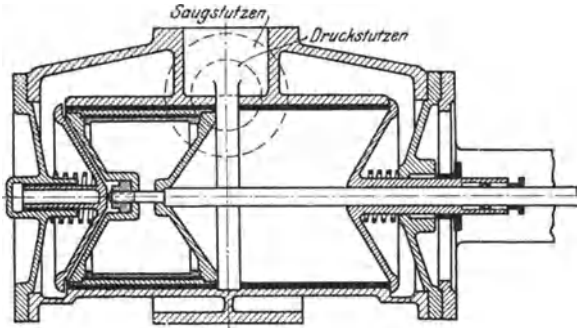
Christie-Kolben-Trockenluftpumpe der Wheeler Condenser and Engineering Co.
